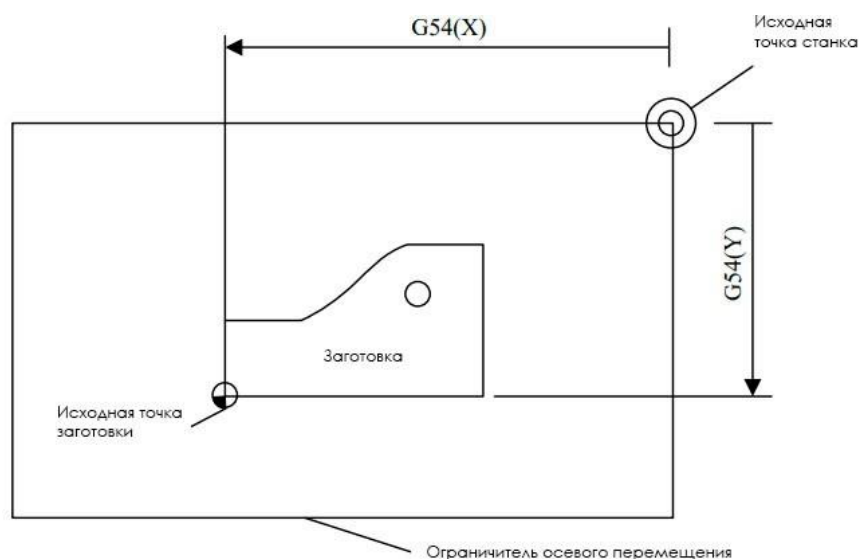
Отношение между коррекцией заготовки и системой координат станка
